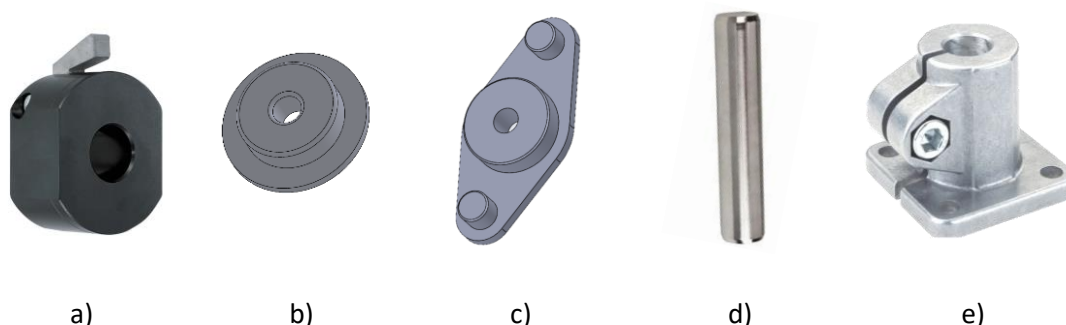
a) bloqueador; b) adaptador de diâmetro; c) suporte da bobine; d) veio/suporte da bobine; e) flange.
